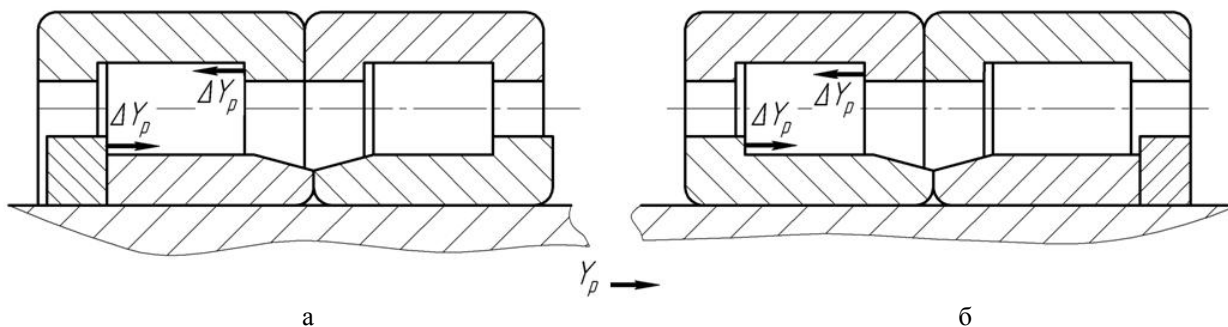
Схемы передачи рамной силы цилиндрическими буксовыми подшипниками
